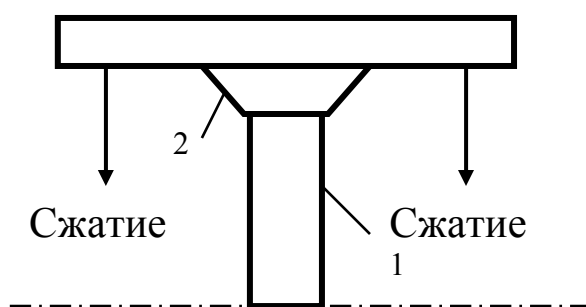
Схема сжатия свариваемых деталей в приспособлении (показана верхняя половина).
